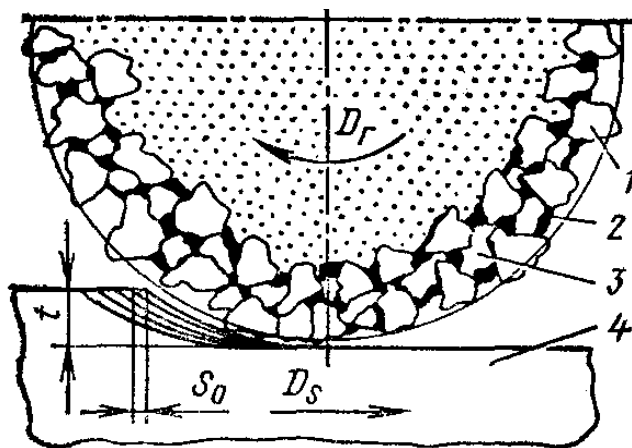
Конструкция шлифовального круга и схема срезания припуска: 1 – зерна; 2 – связка; 3 – поры; 4 – заготовка
